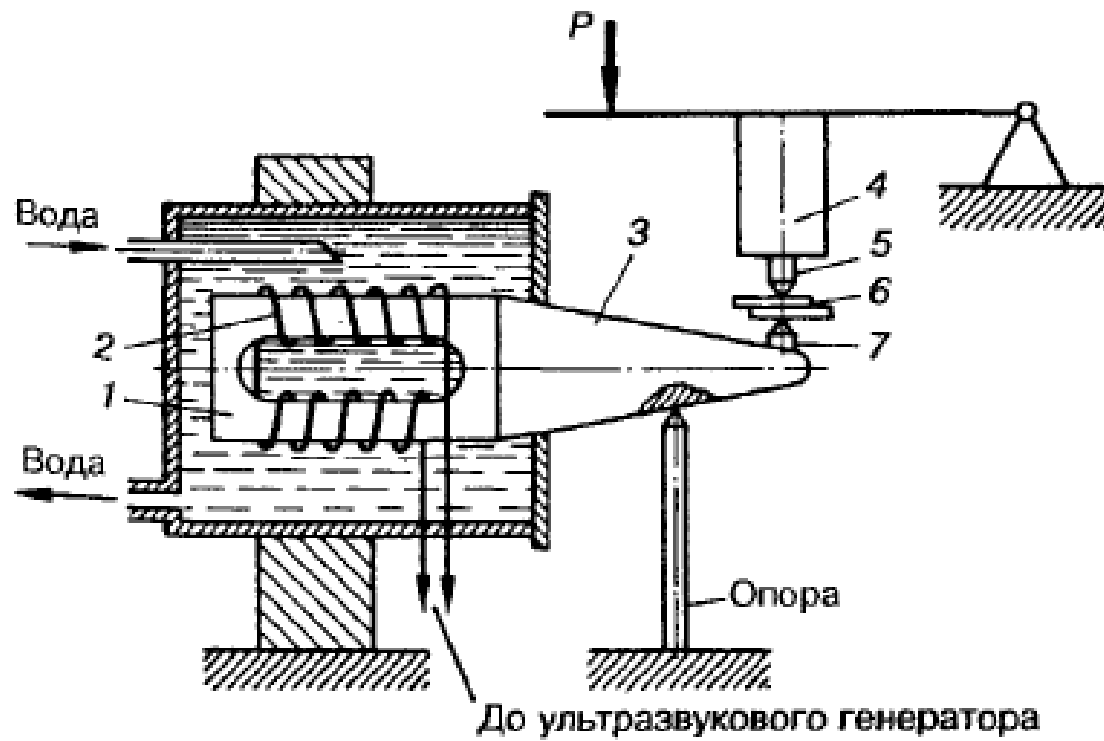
Схема установки для точкового зварювання ультразвуком
